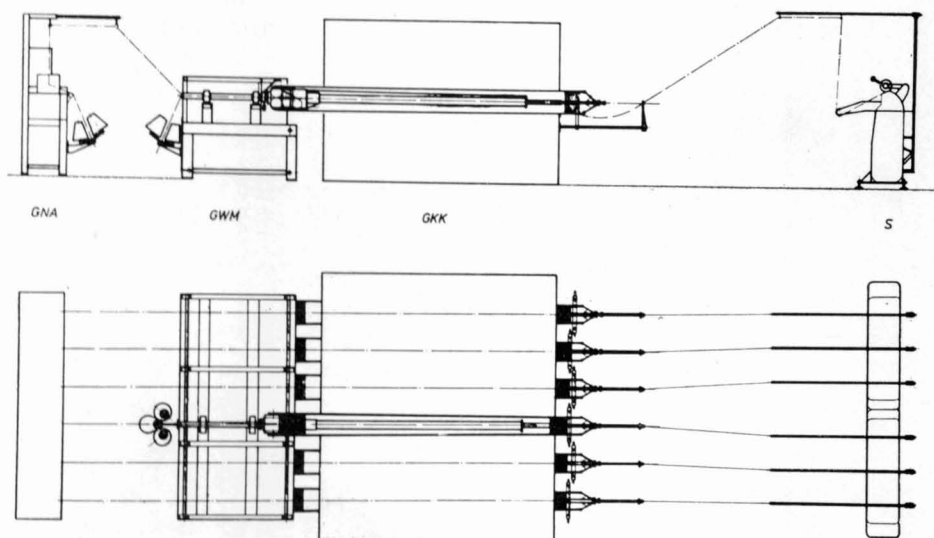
Disposición del conjunto de máquinas para encogimiento y bobinado en continuo de hilo, de la firma Horauf.
